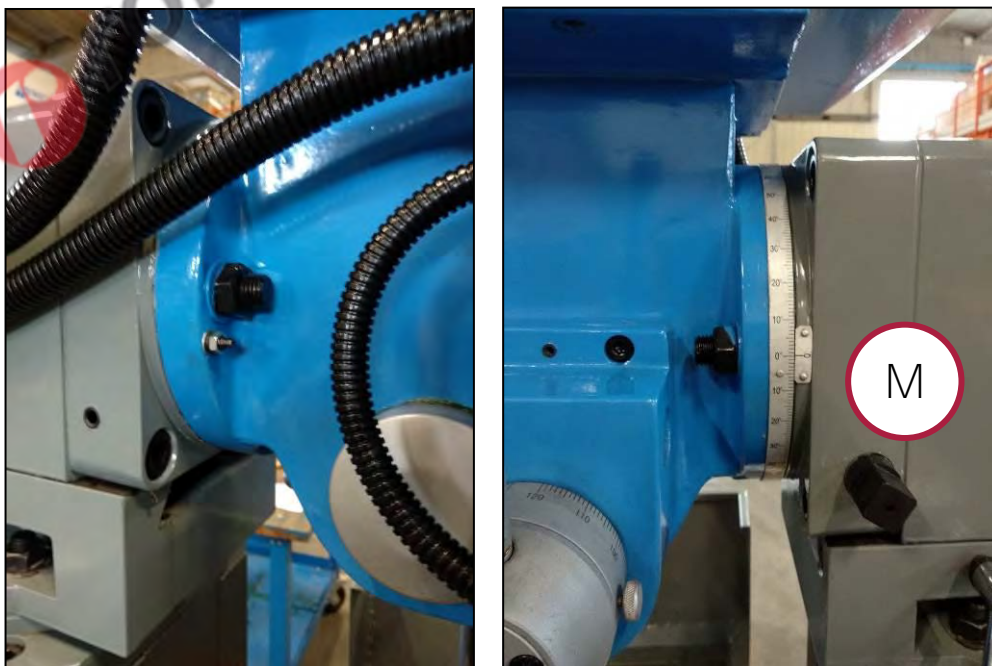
Viti di fissaggio e perno di centraggio della testa.
